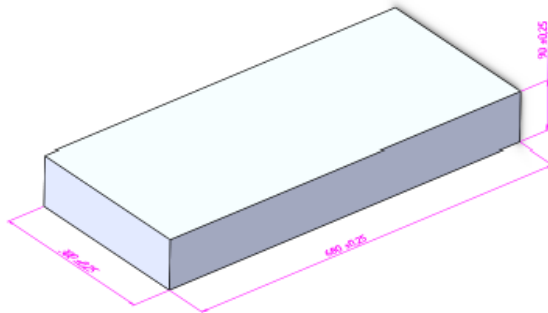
3D-модель заготівлі деталі ливарної прес-форми
